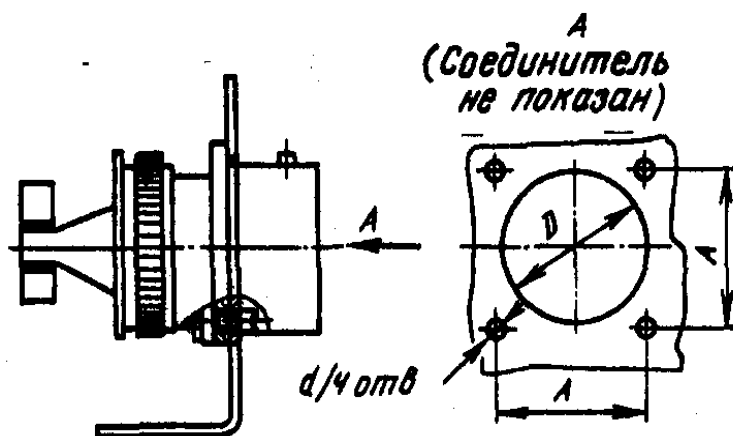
Установка и крепление соединителей СНЦ-23 в корпусах приборов
